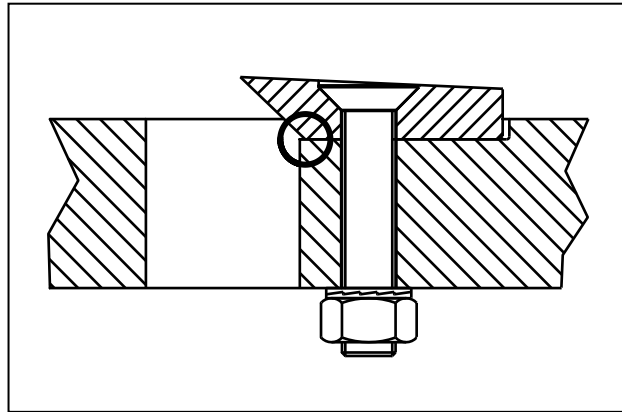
Die Schneidenfläche des Messers hinter dem Loch durch den Rotor
